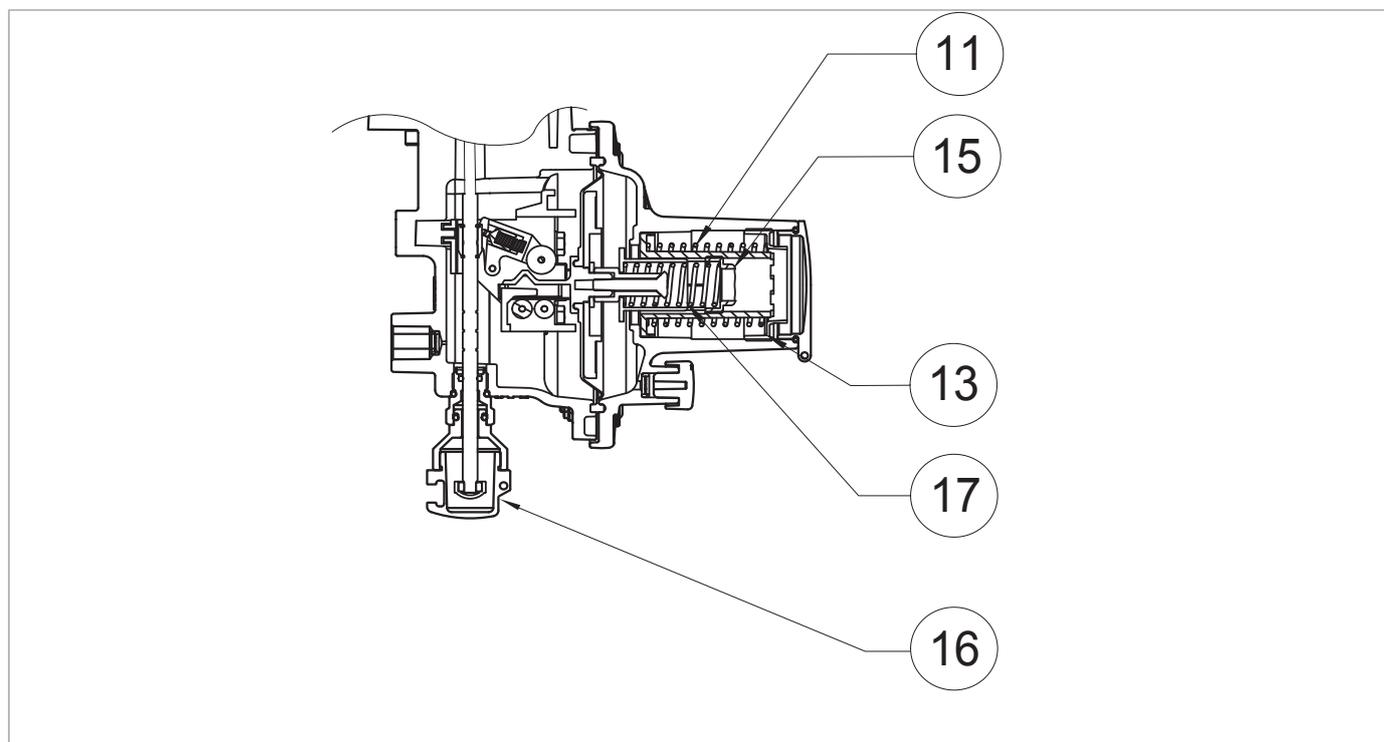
Калибровка реле давления для блочного клапана LA
